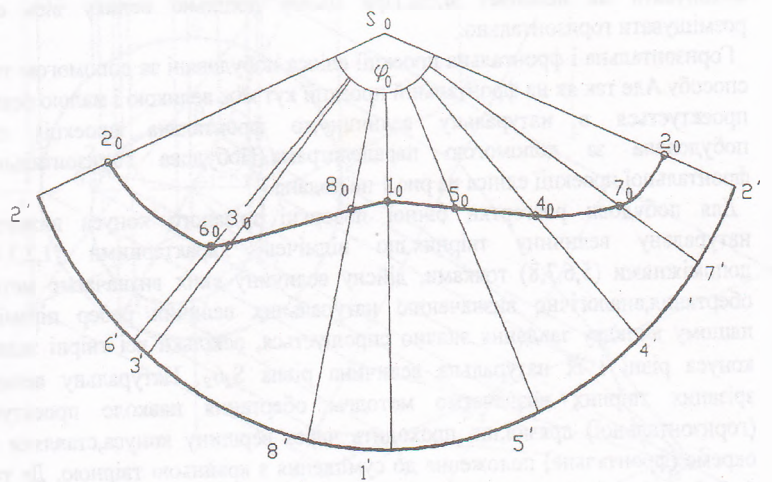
Розгортка бічної поверхні зрізаного конуса.
